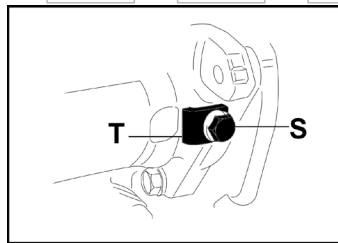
Allentare la vite di fissaggio S della pompa alta pressione, rimuovere la staffa di tenuta T, e serrare la vite di fissaggio S per bloccare la pompa.
